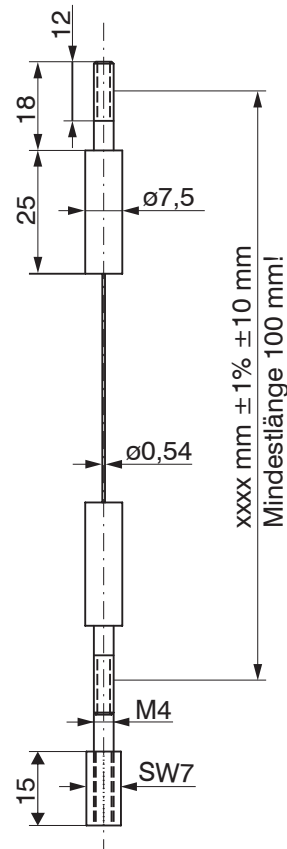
Seilverlängerung WE-xxxx-M4, Abmessungen in mm
